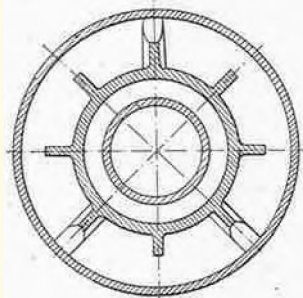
Coupe transversale d'un élément surchauffeur.
